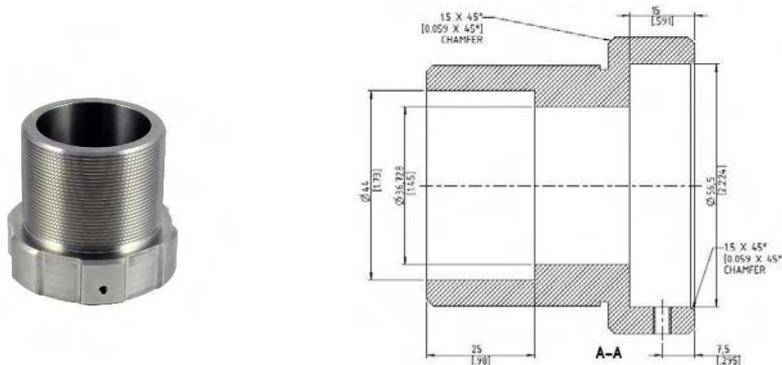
Vue et dimensions du flasque d'adaptation (E-MFA-7)
